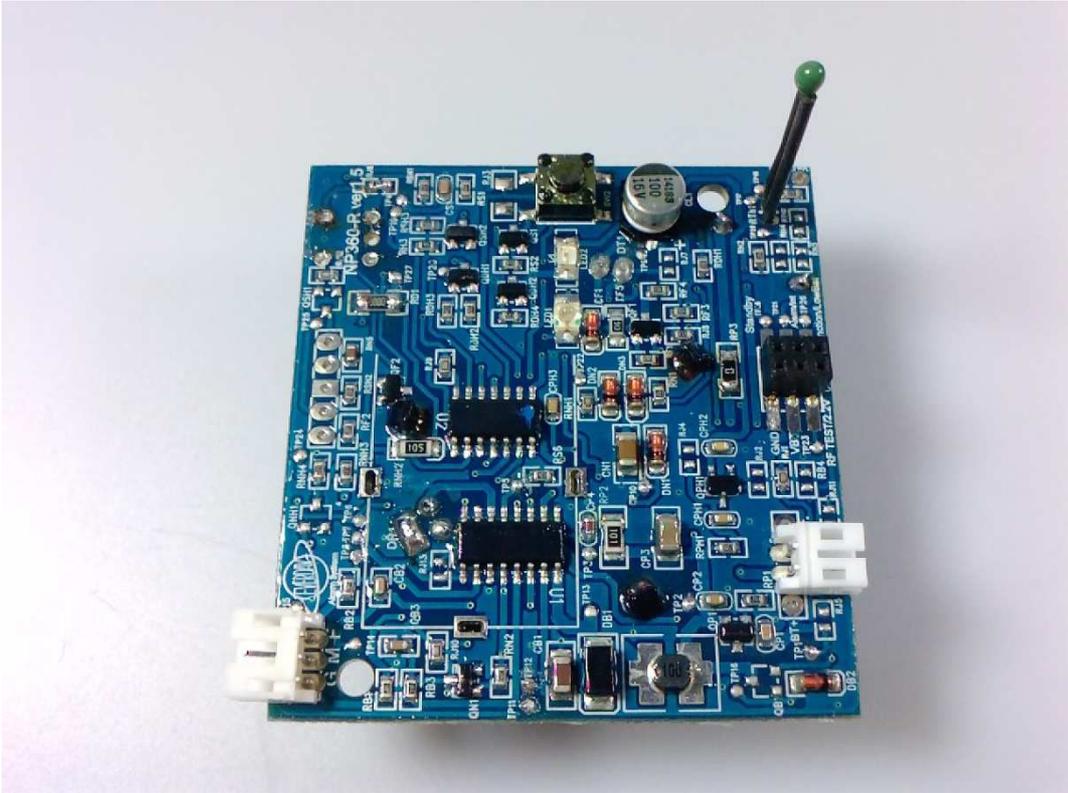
/ Picture 9 Platine mit Temperatursensor / PCB with heat sensor
